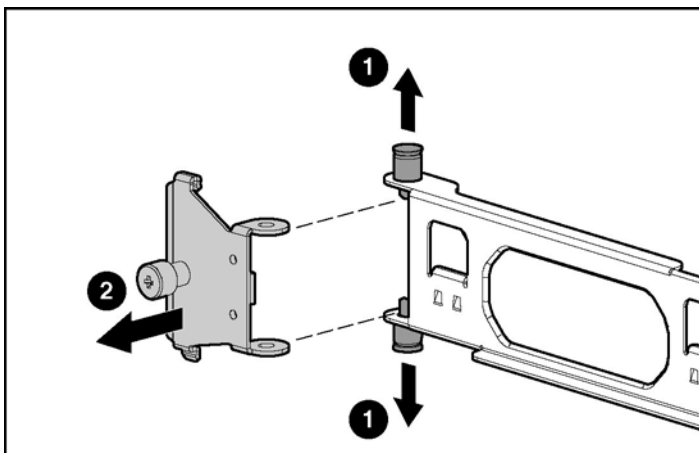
Entfernen der Halterung für eckige Montageöffnungen
